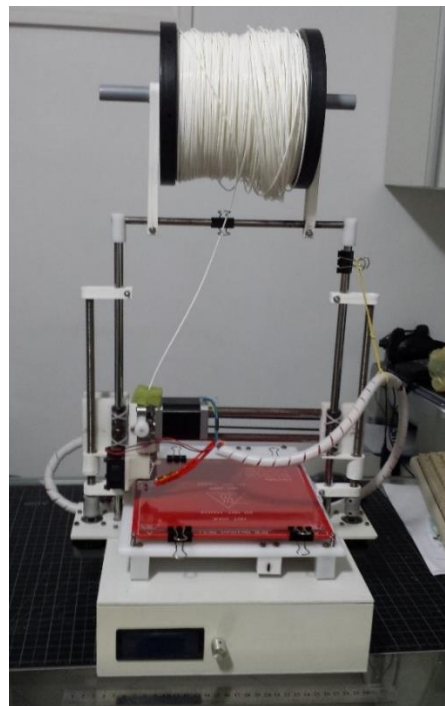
Impressora 3D projetada e construída pelo Autor.
